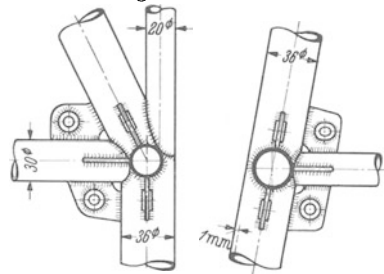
Rohrknoten mit angeschweißten Stegblechen.
